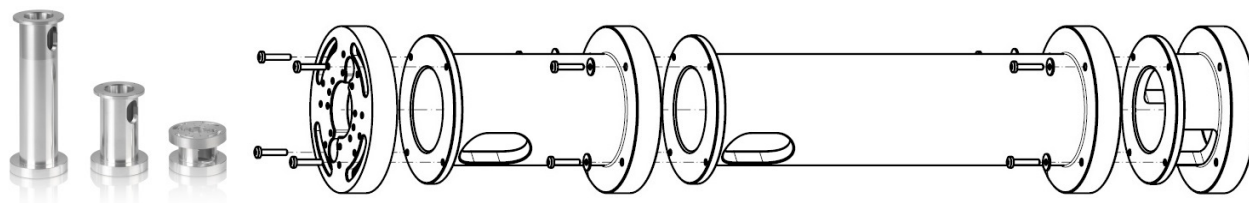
Exemple illustrant un assemblage comprenant tous les tubes métalliques de support
